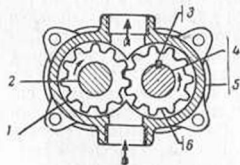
Схема масляного насоса: 1—ведомая шестерня; 2—ось; 3—шпингал, 4—валик; 5—нортуе насоса; 6—ведущая шестерня.
